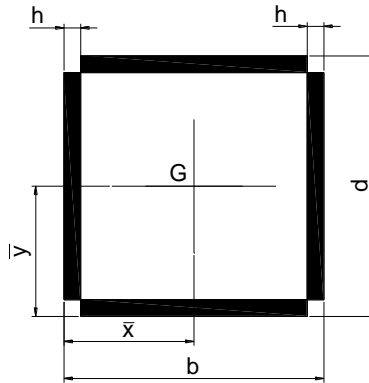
Cordón soldadura anclaje superior - Chasis
